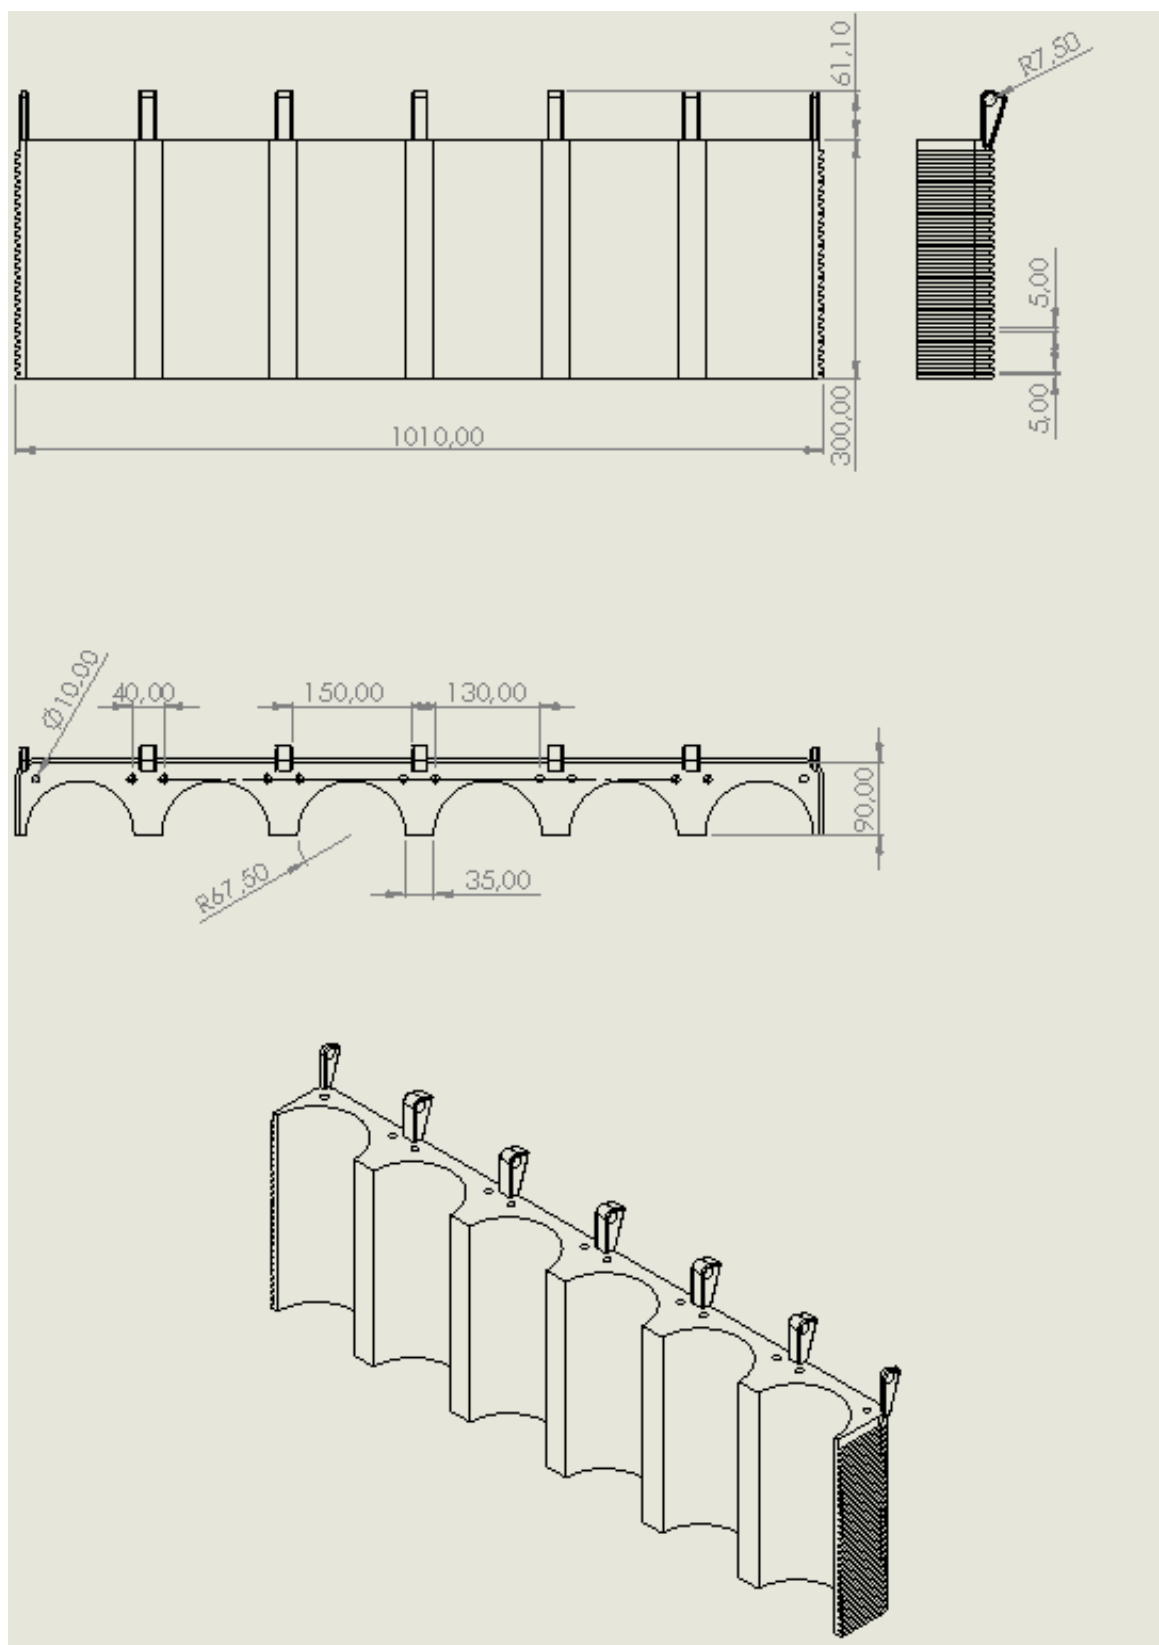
Plano de los cilindros del 6-L, escala 1:7
